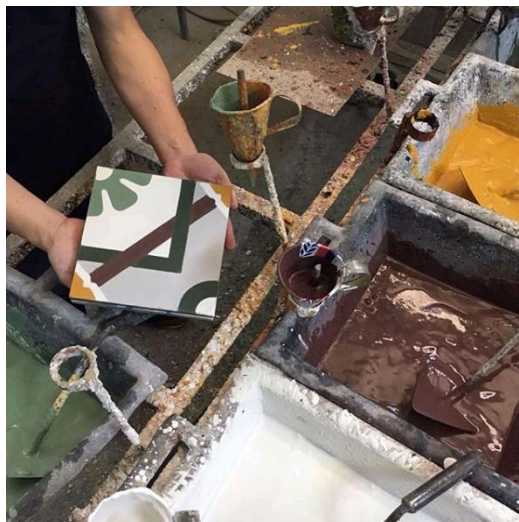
Vue générale de procédé de fabrication d'un carreau de ciment
